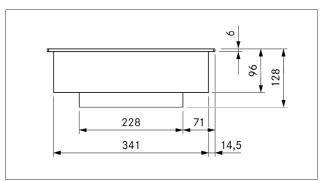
Dimensões do aparelho PKIW3, vista dianteira
